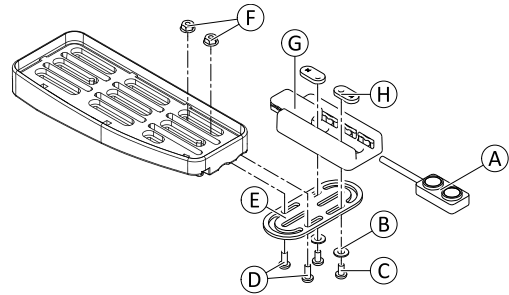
Le montage latéral de la commande double sert d'exemple.
